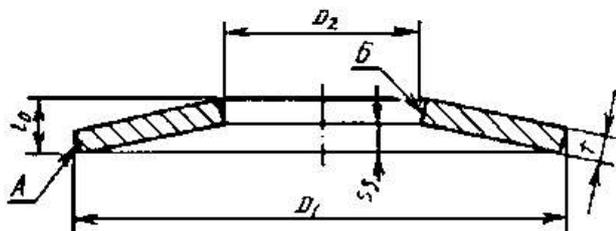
Схема тарельчатой пружины, изготовленной по ГОСТ 3057-90
